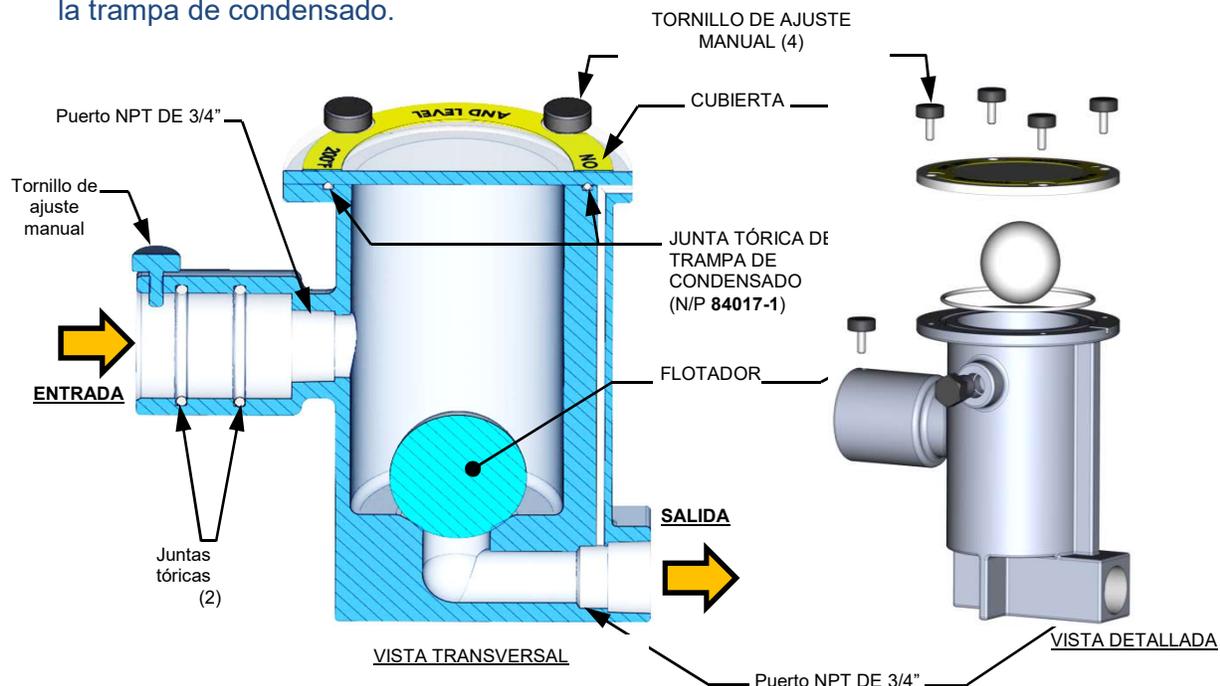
Trampa externa de condensado. Vista transversal y detallada
